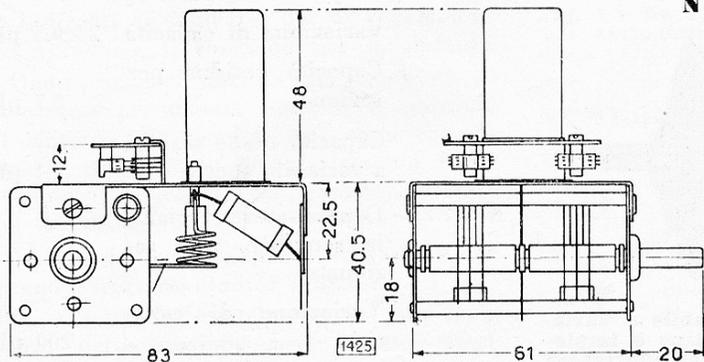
Le dimensioni di ingombro del gruppo A.F. n. 2691.
